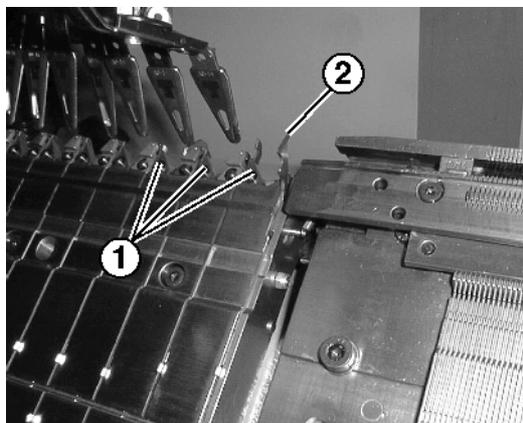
Dispositivo de pinzado y corte del hilo
